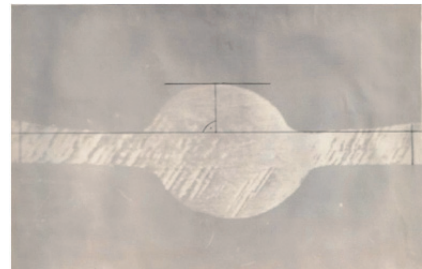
Поперечное сечение контрольной поковки после изготовления 1600 деталей, образец №6'
